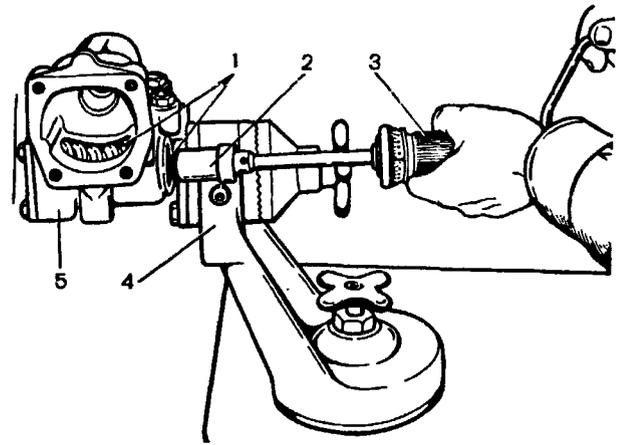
Контроль момента трения червяка динамометром: 1 - червяк; 2 - головка А.95697/5; 3 - динамометр 02.7812.9501; 4 - кронштейн стенда для ремонта картера рулевого механизма; 5 - картер рулевого механизма
